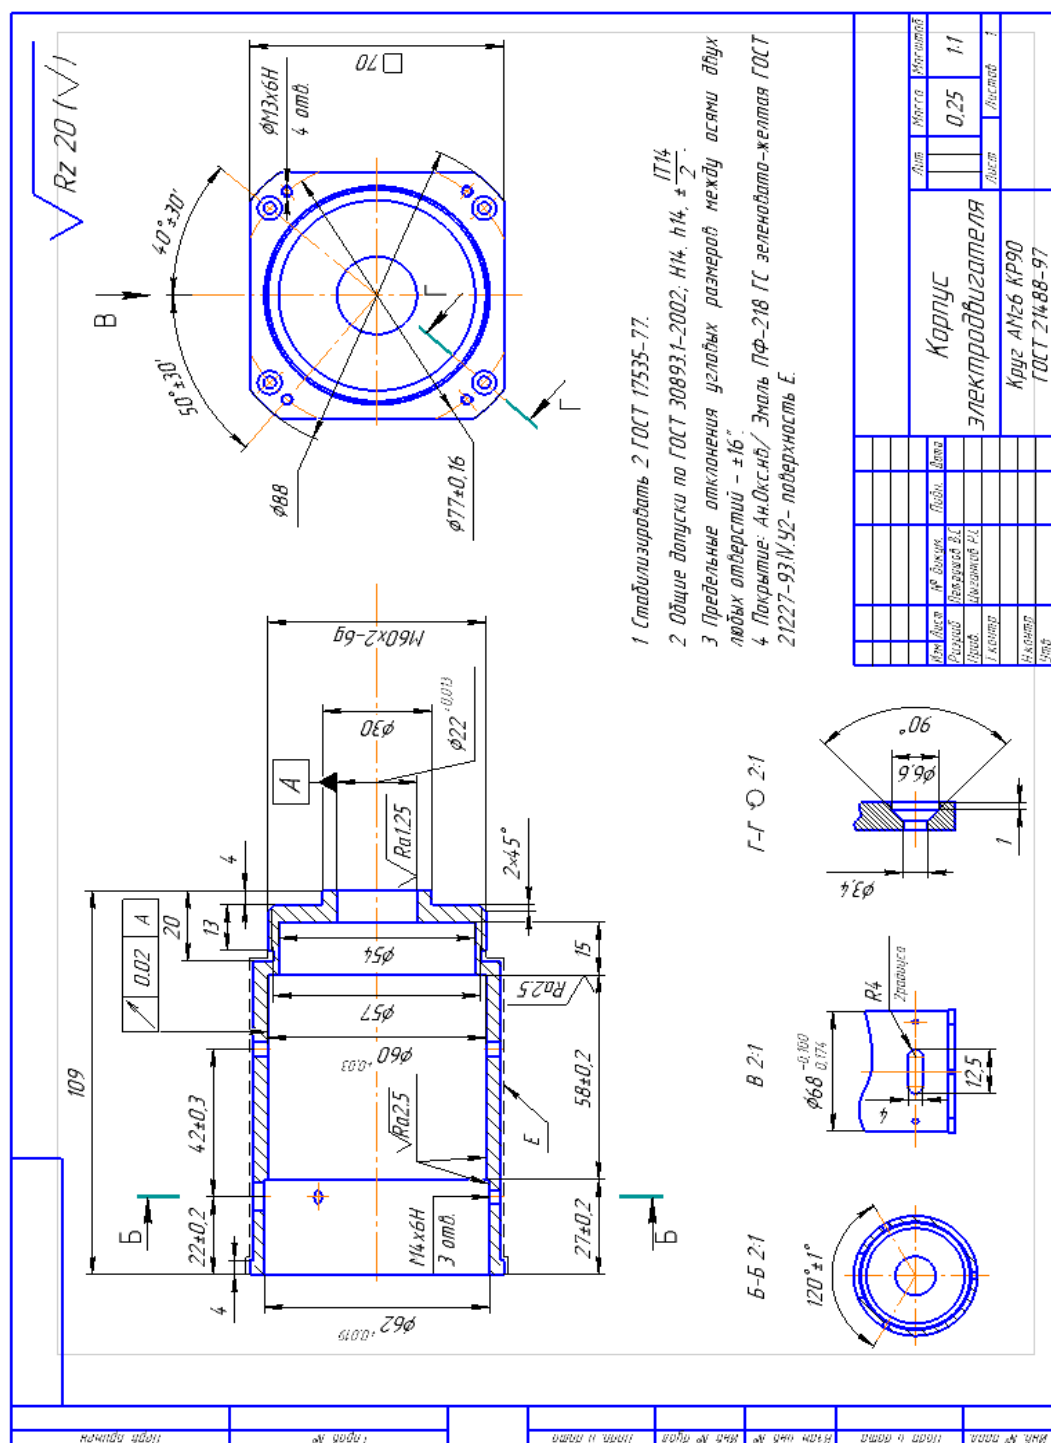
Чертеж детали «Корпус электродвигателя»
